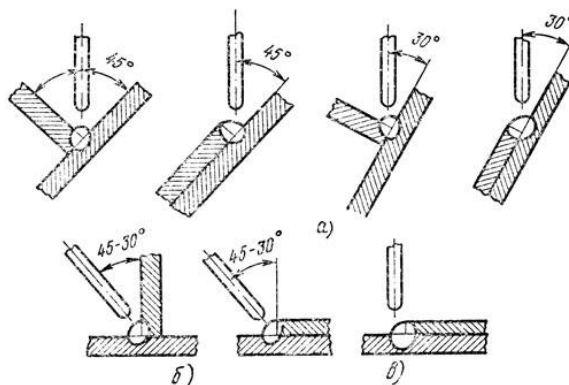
Способы выполнения угловых, тавровых и нахлесточных швов: а - сварка в симметричную и несимметричную 'лодочку', б - наклонным электродом, в - сварка с оплавлением кромки
